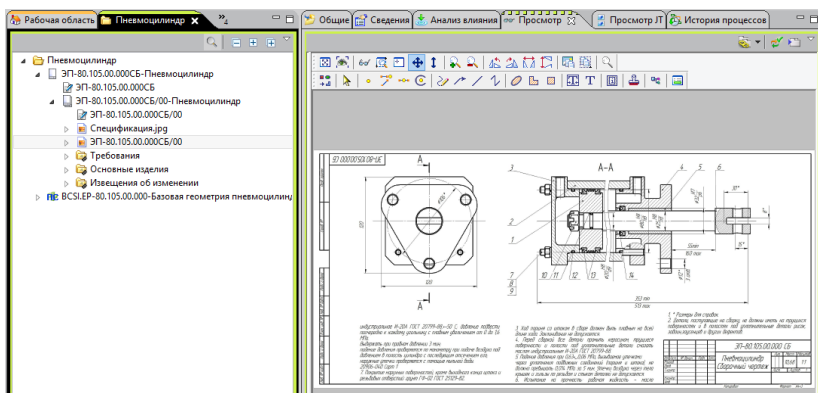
Сборочный чертеж пневмоцилиндра
